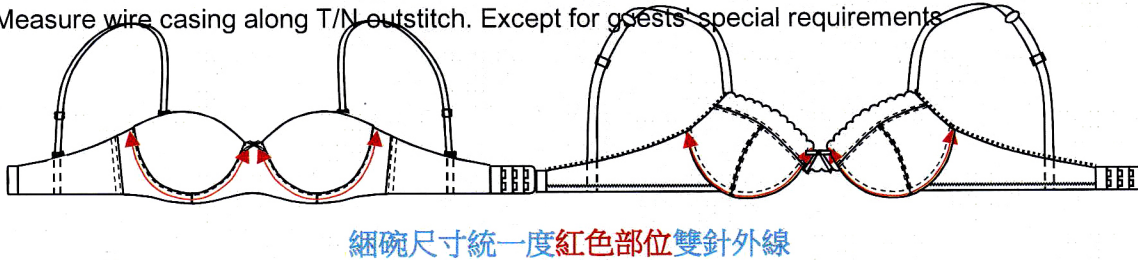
統一所有網碗長尺寸只能做正公差. 鋼圈虛位按正常做, 尺寸表要寫正公差. (见下图)
